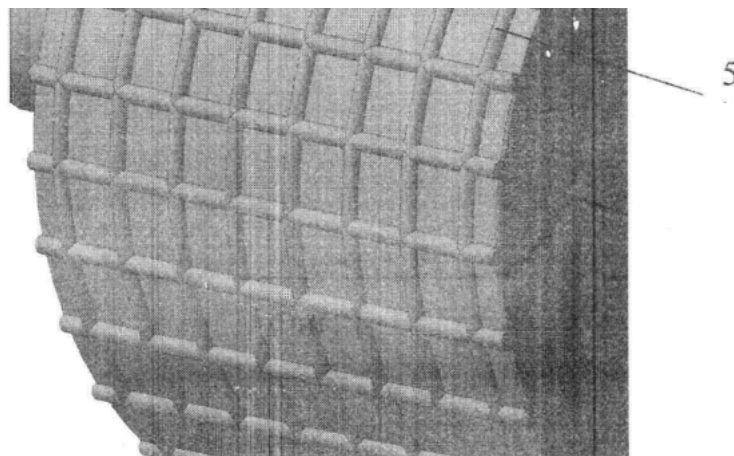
Валок четырёхвалковой дробилки [3]:
